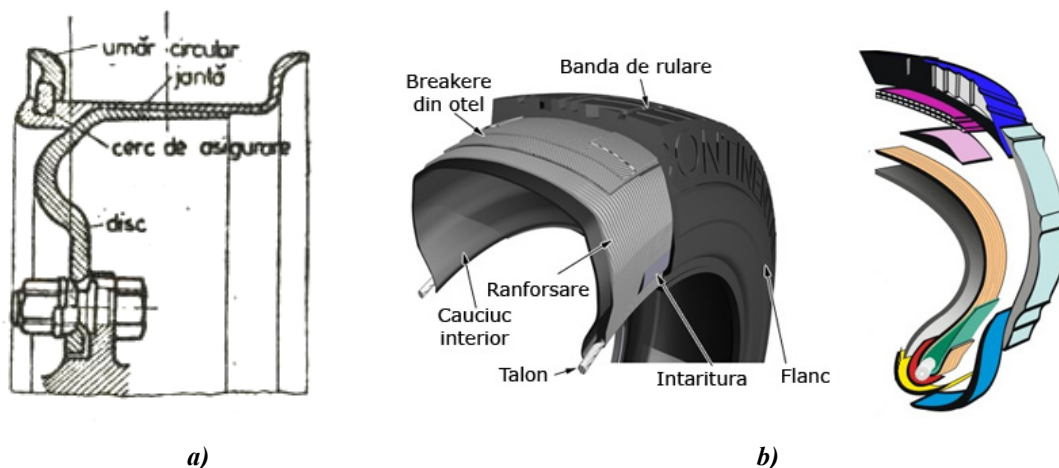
Elemente structurale: a) roată, b) anvelopă.
